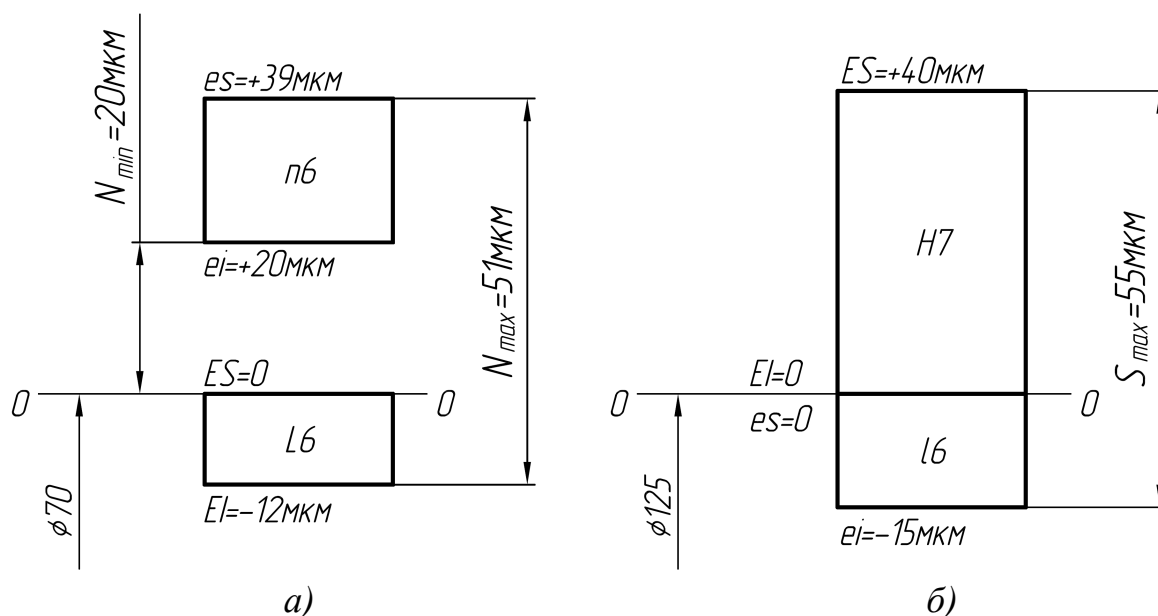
Схема посадок: а) внутрішнє кільце – вал; б) зовнішнє кільце – корпус
